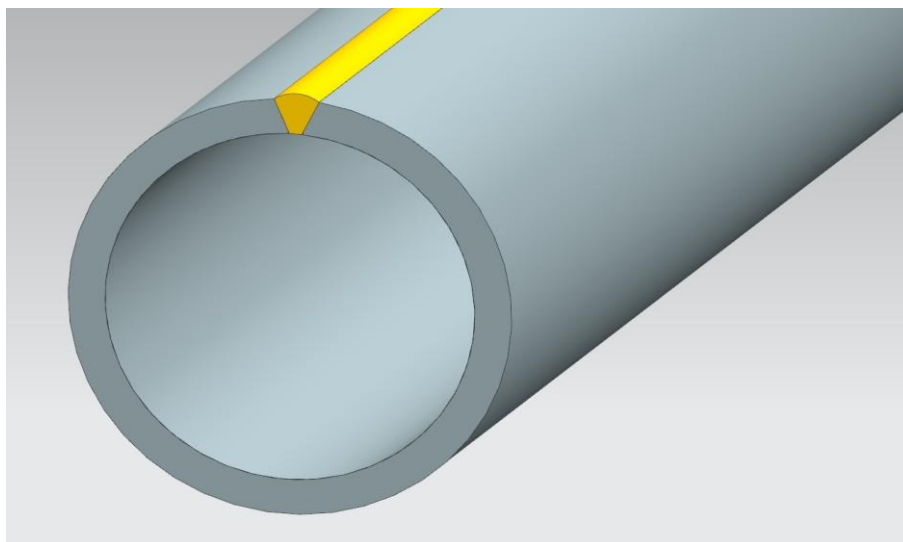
Сварка одиночных граней на примере продольного шва трубы
